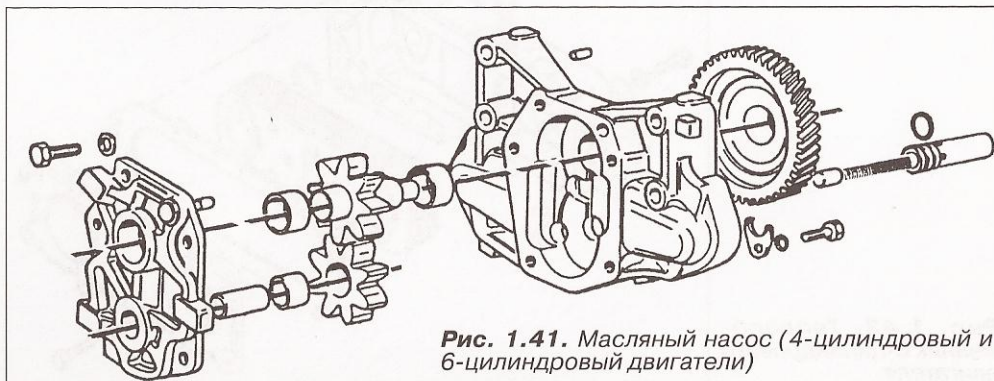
Масляный насос (4-цилиндровый и 6-цилиндровый двигатели)
